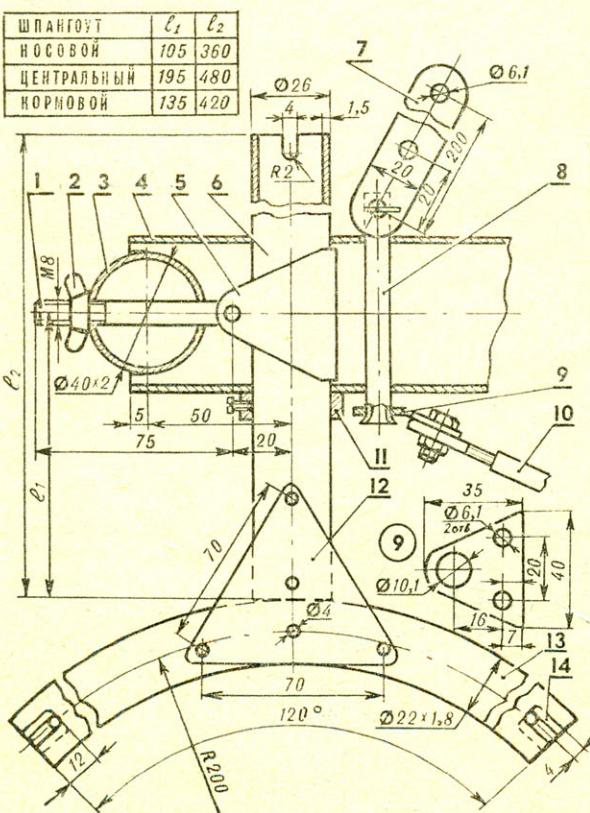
Типовой соединительный узел шпангоута, стрингера и поперечной балки:
